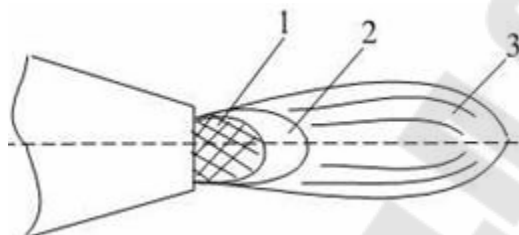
Схема газового пламени: 1 – ядро пламени; 2 – рабочая зона; 3 – факел
